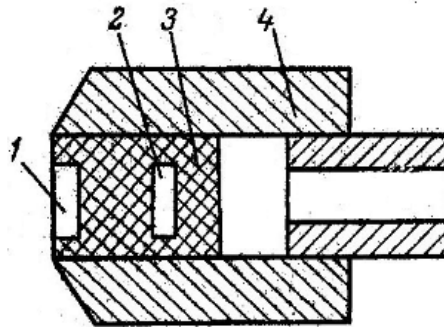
Конструкція п'єзоелектричного лічильника з компенсаційним п'єзоперетворювачем: 1,2 – вимірювальний і компенсаційний п'єзоперетворювачі; 3 – ізолятор; 4 – корпус.
